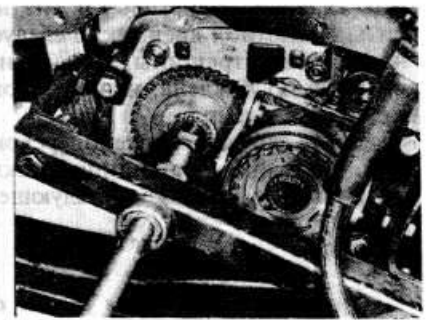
Разъединение ведущего вала и сцепления с помощью приспособления
